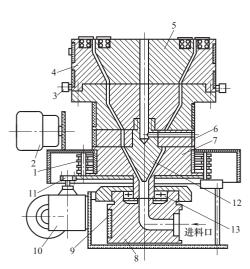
十字形直角式进料旋转机头 1—换向接触环 2—热电表 3—调节螺钉 4—口模 5—芯模 6—芯模支架 7—机头体 8—连接体 9—轴承部件 10—传动装置 11—齿轮 12—分流锥 13—轴承
